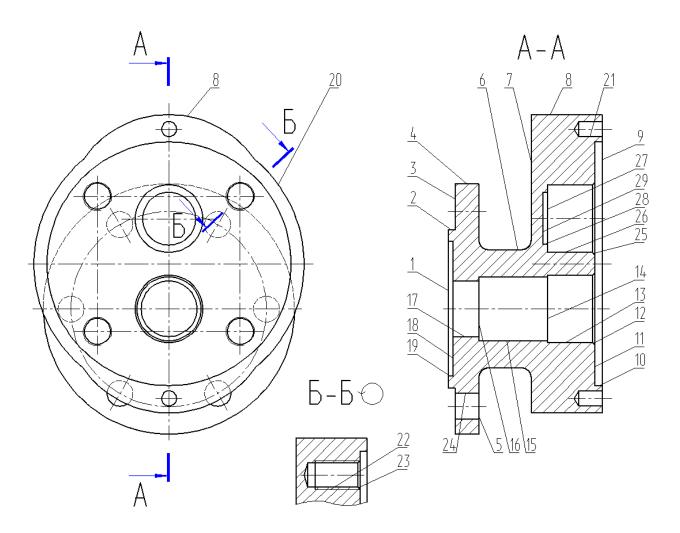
Систематизация поверхностей детали «Корпус гидромотора»
